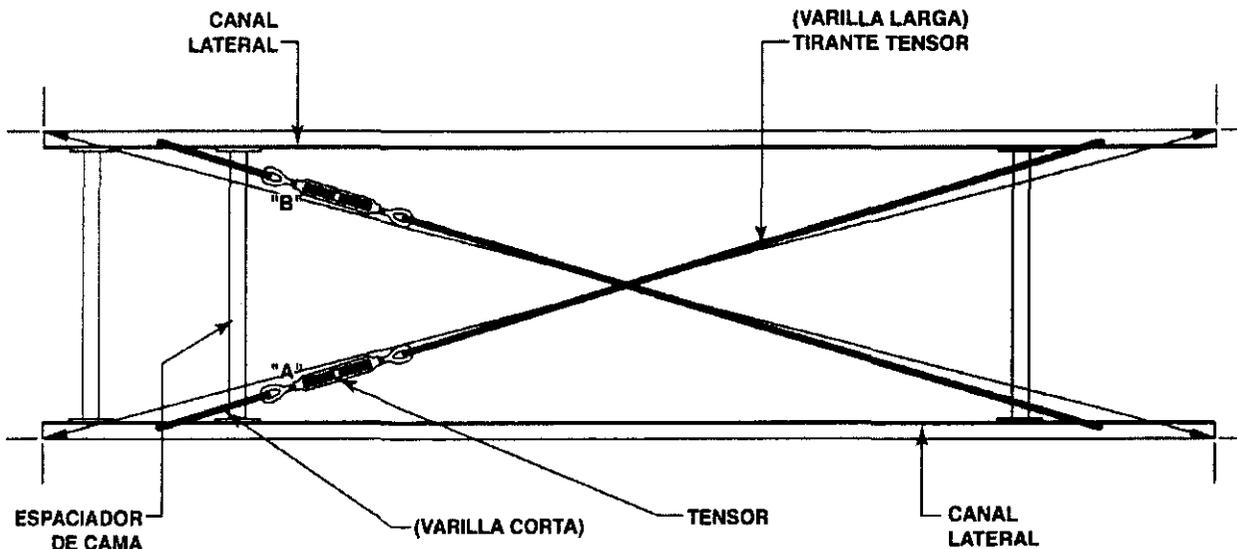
Ubicación del Tirante Tensor Transversal.
